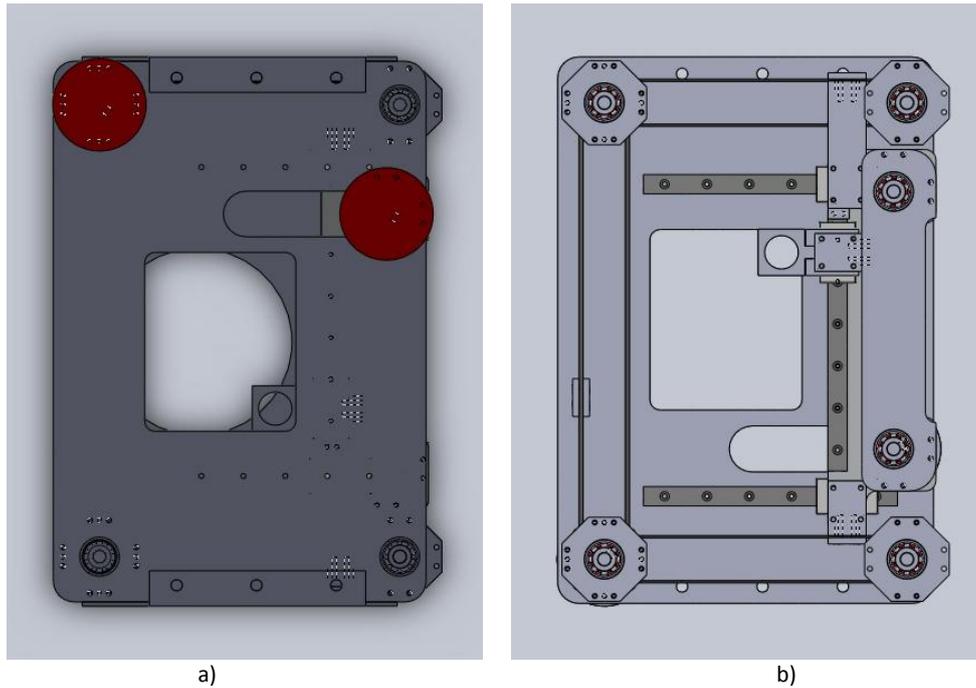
Sistema na posição de marcha atrás. a) Vista de cima. b) Vista de baixo.
